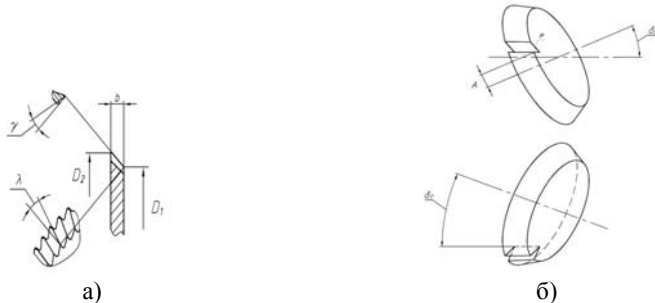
Формирование режущей части фрезы: а) режущая часть угловой фрезы с ненулевой геометрией; б) схема образования зубьев фрезы.
